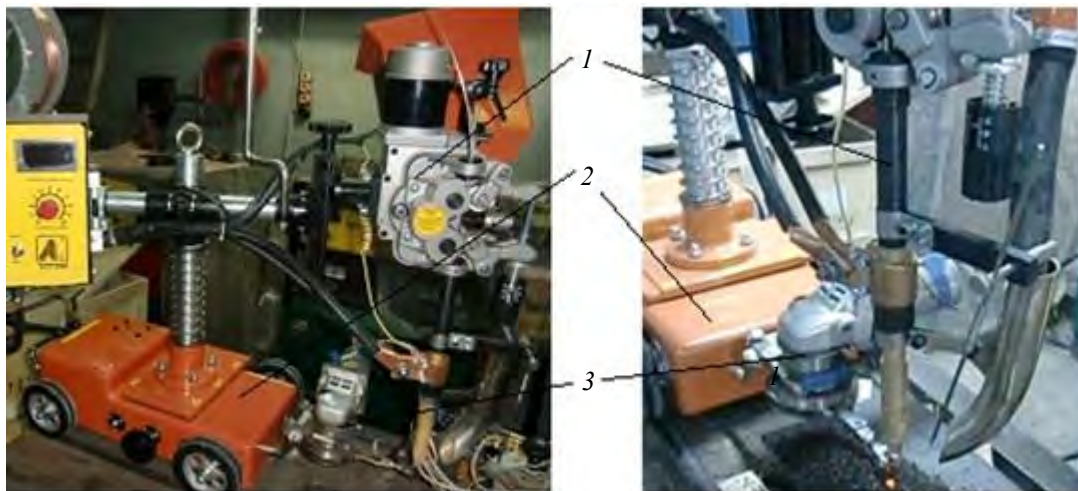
Сварочный трактор с механическим генератором для импульсного воздействия на электродную проволоку: 1 – сварочная головка; 2 – каретка трактора; 3 – механический генератор
